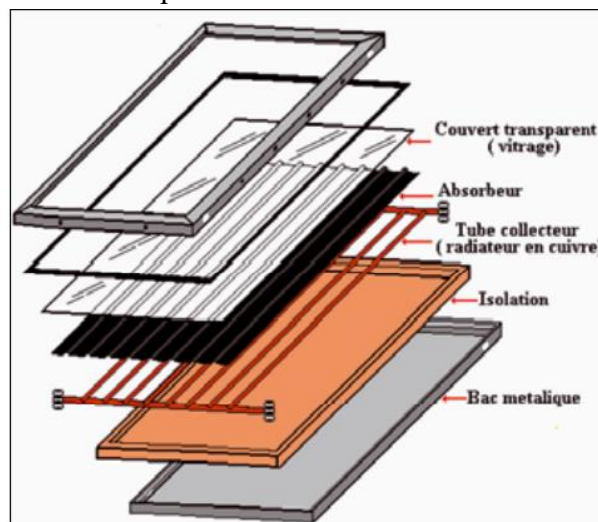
Coupe schématique d'un capteur plan vitré [22]
